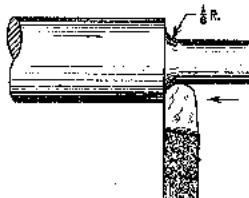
Torneado de una solera con rincón de radio pequeño.
